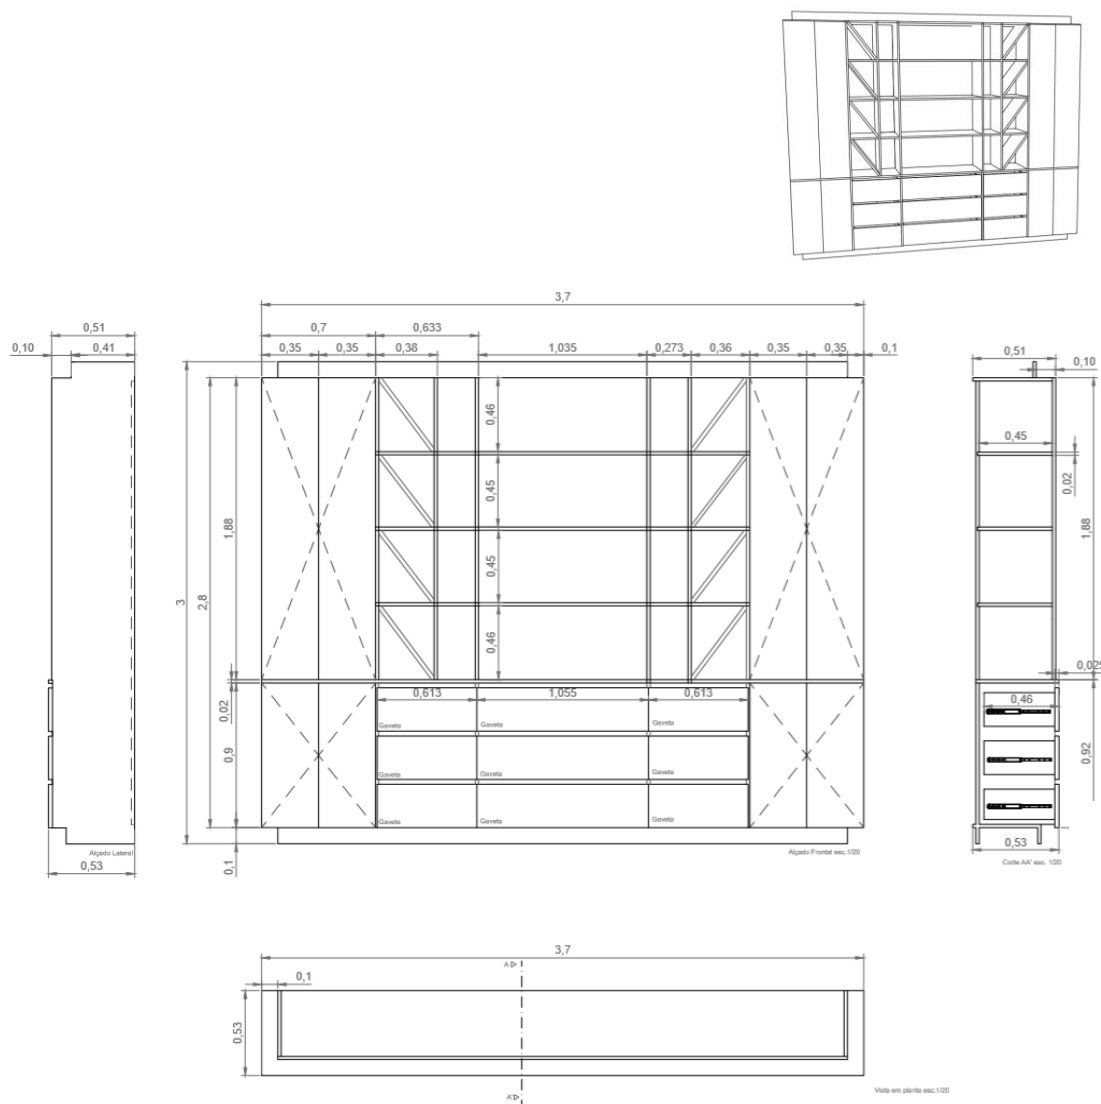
Desenho Técnico M01 - v1. Escala 1/20 Fonte: autor
